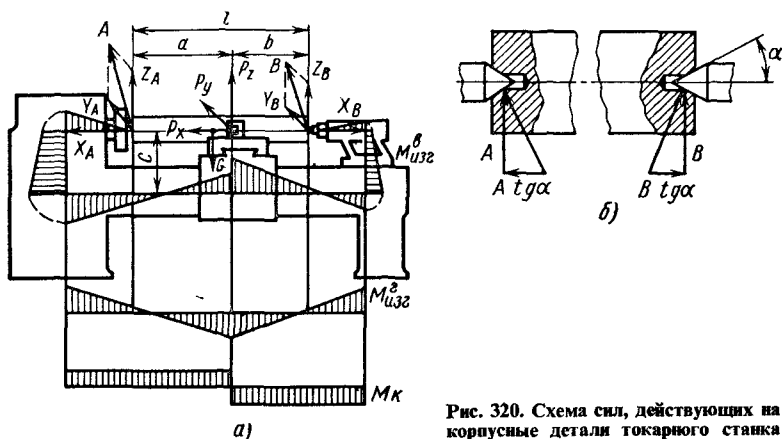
Схема сил, действующих на корпусные детали токарного станка
